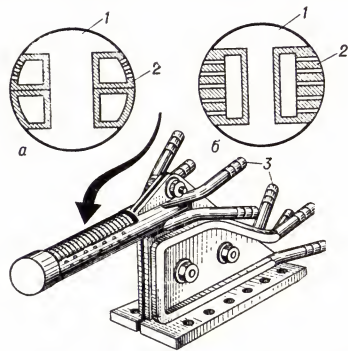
Петлевой индуктор для закалки внутренних цилиндрич. поверхностей способом одновременного нагрева при вращении закаливаемой детали: а — конструкция с отдельными камерами для охлаждения индуктора и выхода закалочной воды; б — конструкция без постоянного охлаждения; 1 — магнитопровод; 2 — индуктирующий провод; 3 — трубопровод водяного охлаждения.
